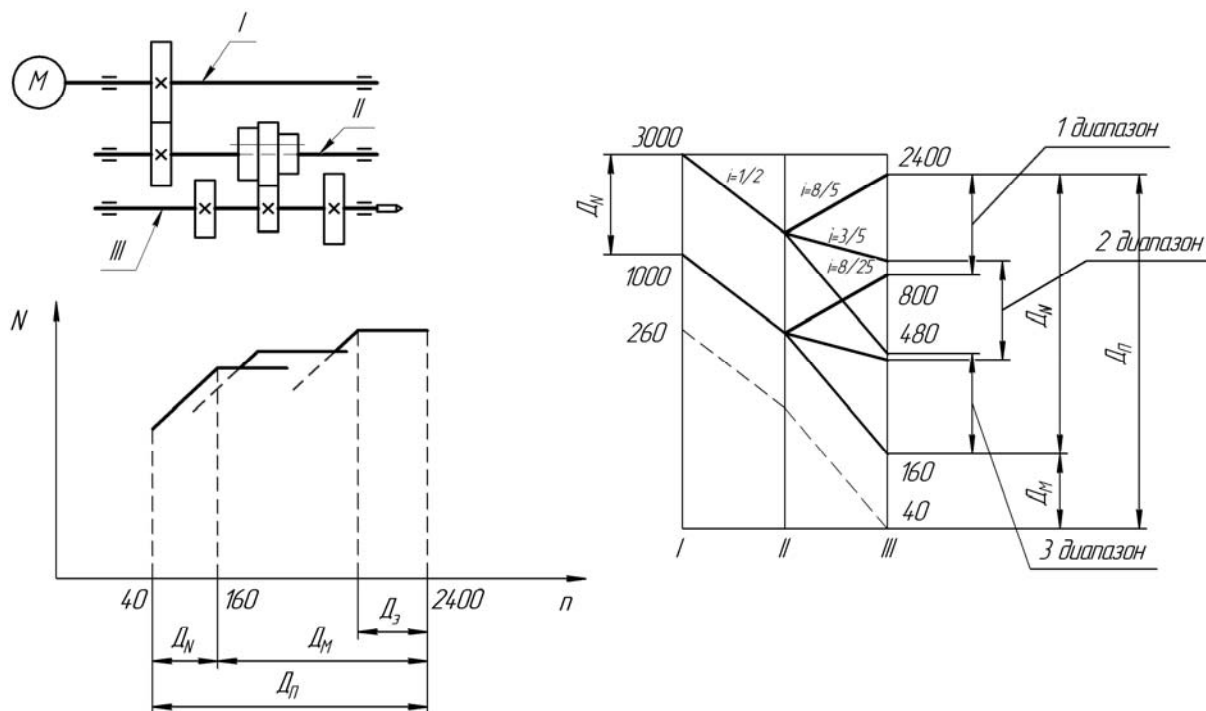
Привод главного движения станка с регулируемым двигателем
